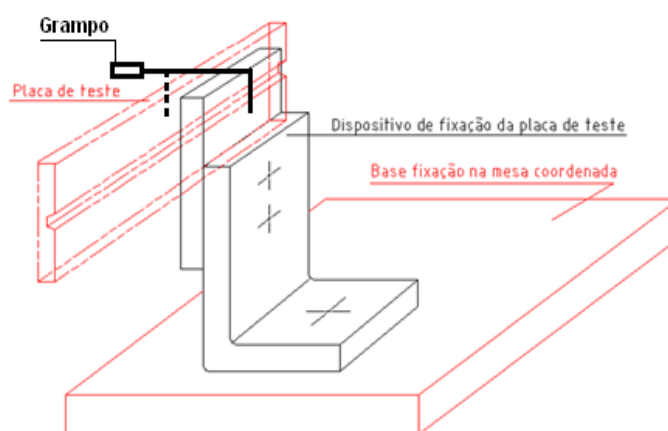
Desenho esquematizado do dispositivo para fixação da placa de teste.
